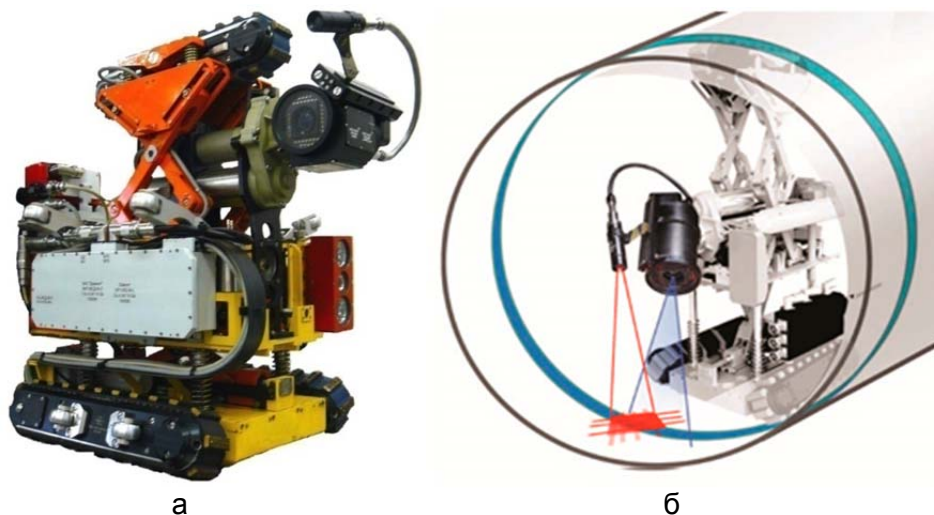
Мобильный модуль для визуально-измерительного контроля: внешний вид (а);
